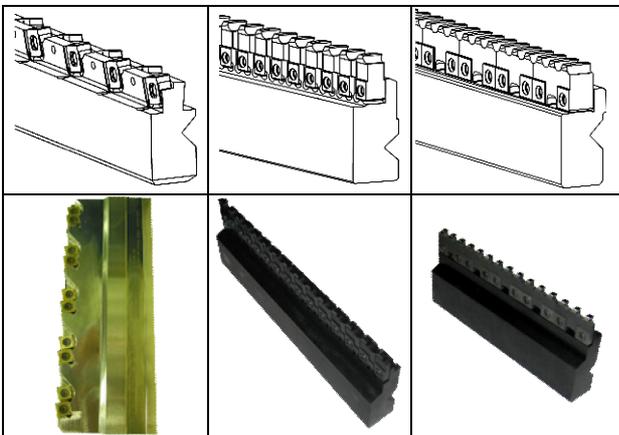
Эскизы предварительно разработанных конструкций протяжек и изготовленные образцы
